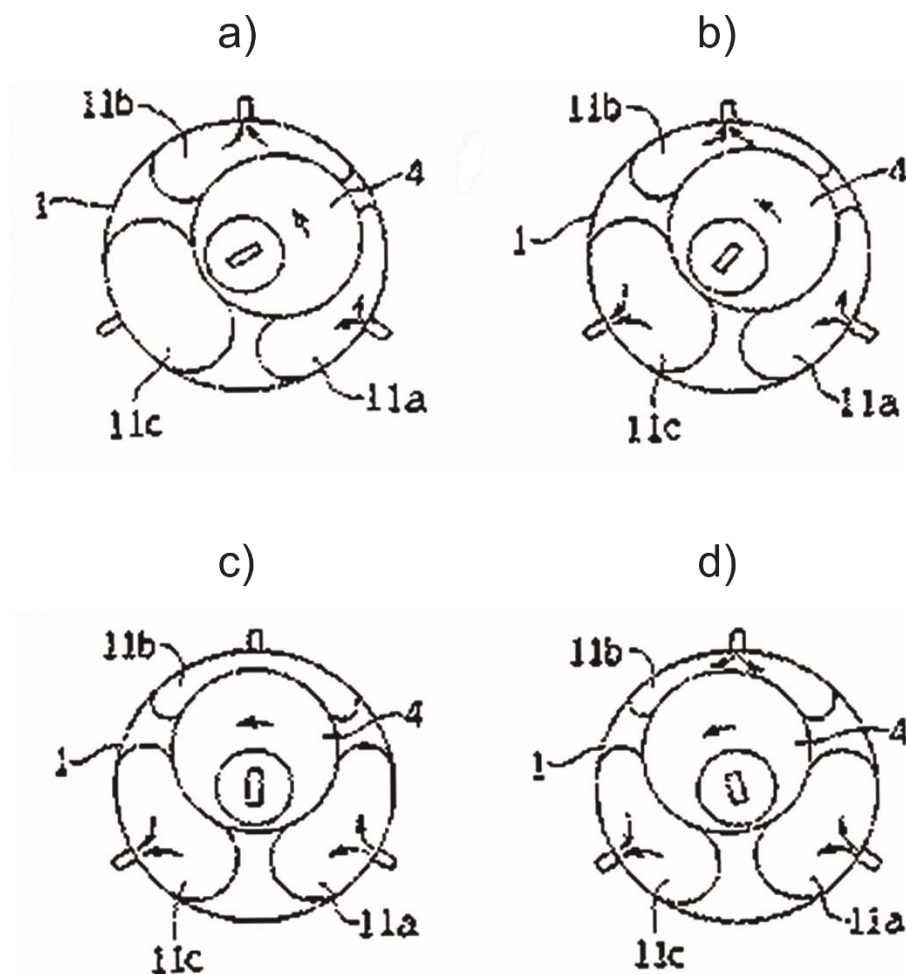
Konstrukce pneumotoru dle Patentu JPS63105280 v podélném řezu, převzato z [11]
